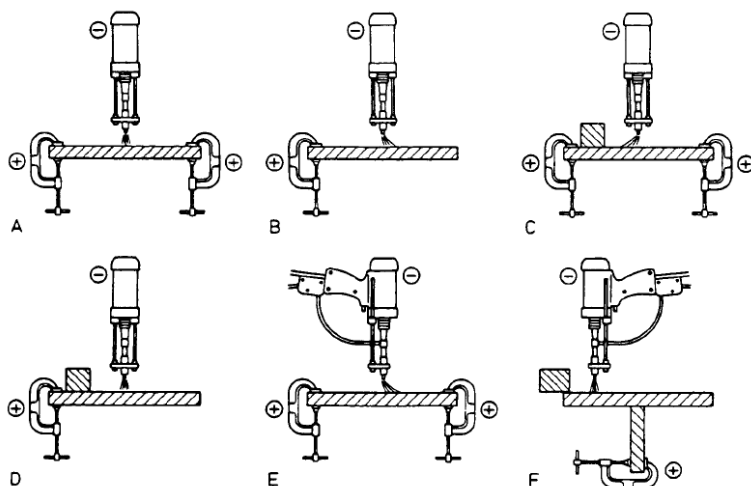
Representação esquemática de uma máquina de soldagem por arco de pinos sob pressão (norma DVS 0902).
